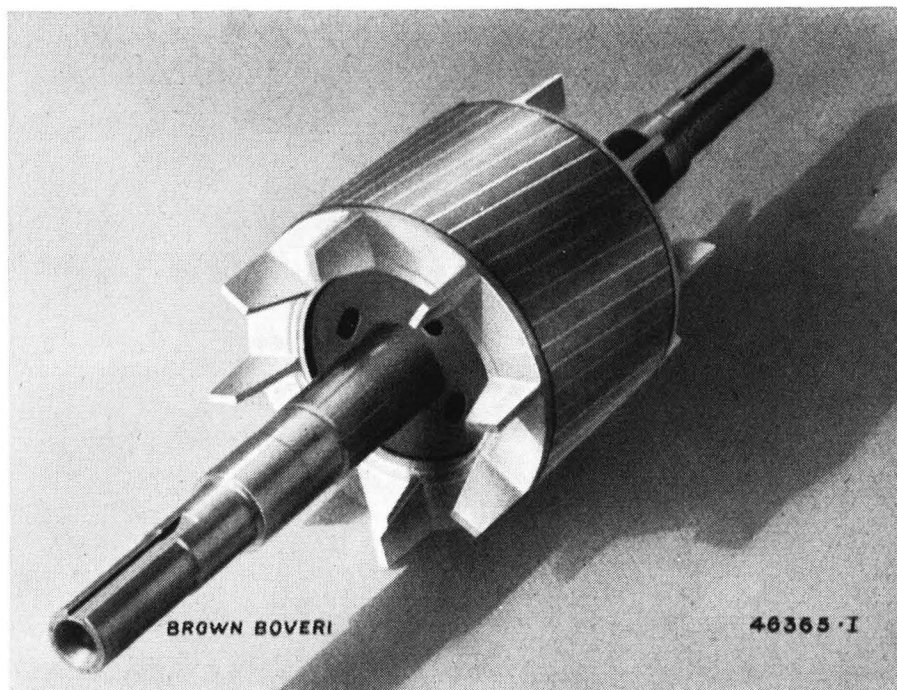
Rotor mit eingegossener Aluminium-Wicklung für Dreiphasenmotor, 15 kW, 2890 U/min.
